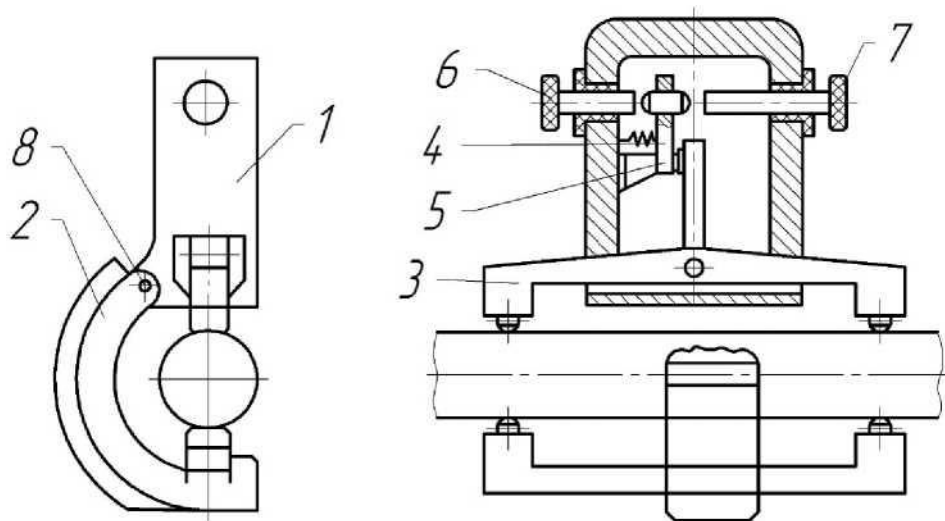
Прилад для вимірювання конусності циліндричної поверхні
